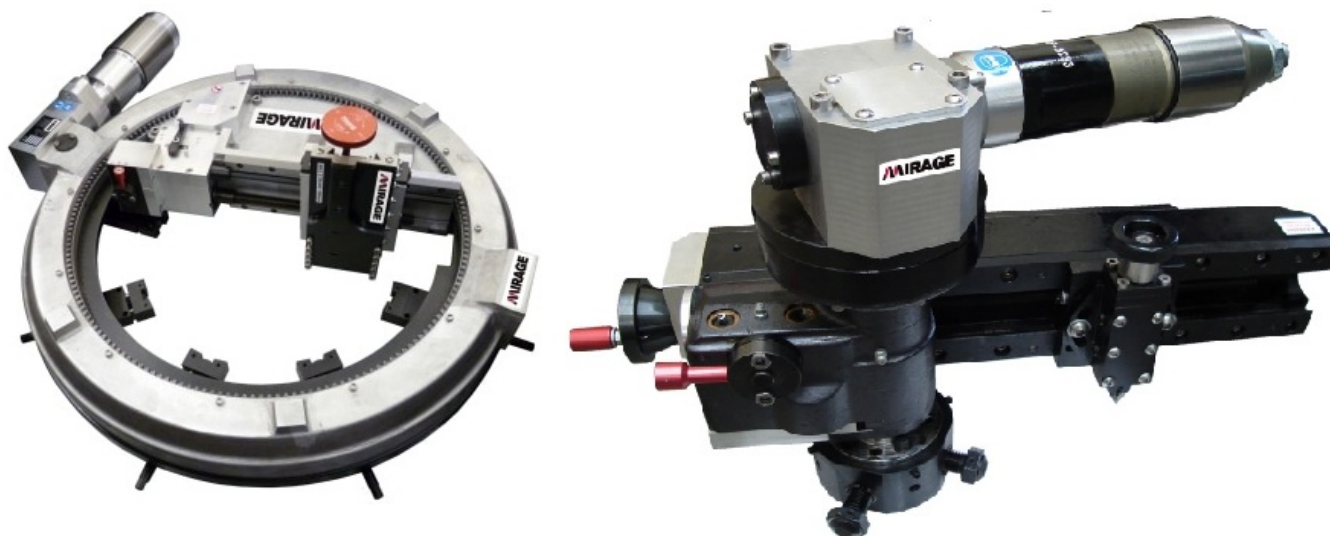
Мобильные станки для обработки фланцев труб [51, 52]
